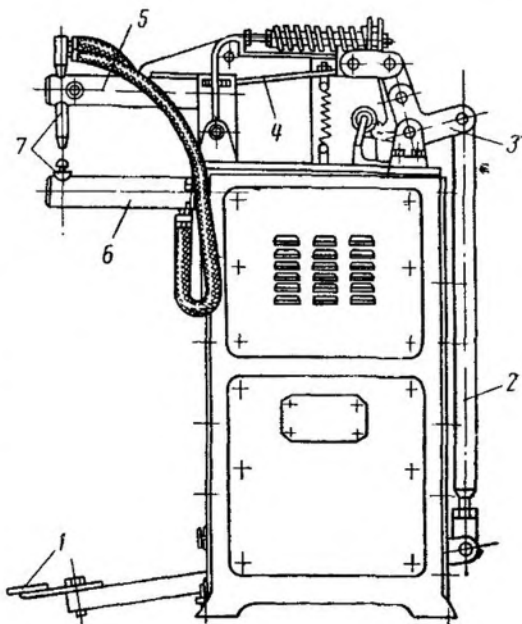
Машина точечной сварки модель АТП-50
